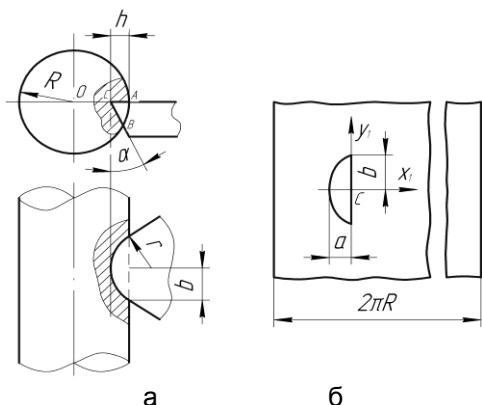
Схема врезания резца в деталь (а), граница отпечатка резца на плоскости развертки поверхности цилиндра (б)
